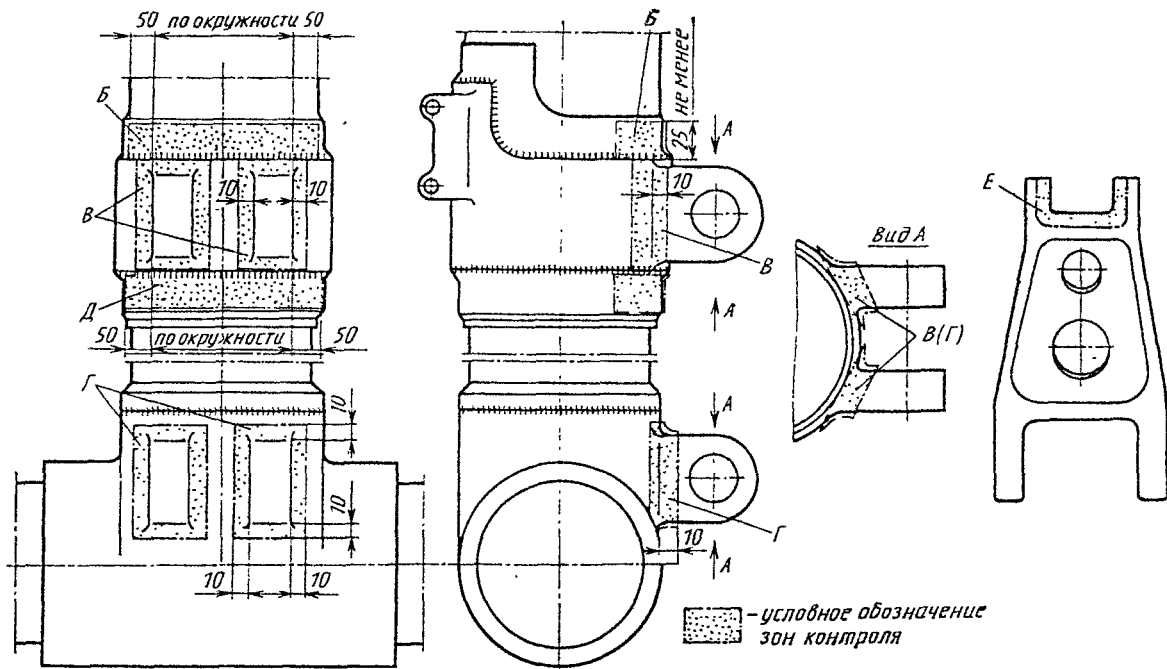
Зоны контроля цилиндра, штока и нижнего звена шлиц-шарнира основной опоры 24-4101-0А
